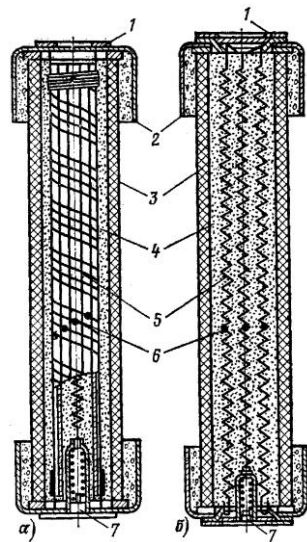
Предохранитель типа ПКТ. а — на ток до 8 А; б — на ток более 8А; 1 — торцевая крышка; 2 — латунный колпачок; 3 — фарфоровая трубка; 4 — кварцевый песок; 5 — плавкая вставка; 6 — шарики из олова; 7 — указатель срабатывания.
